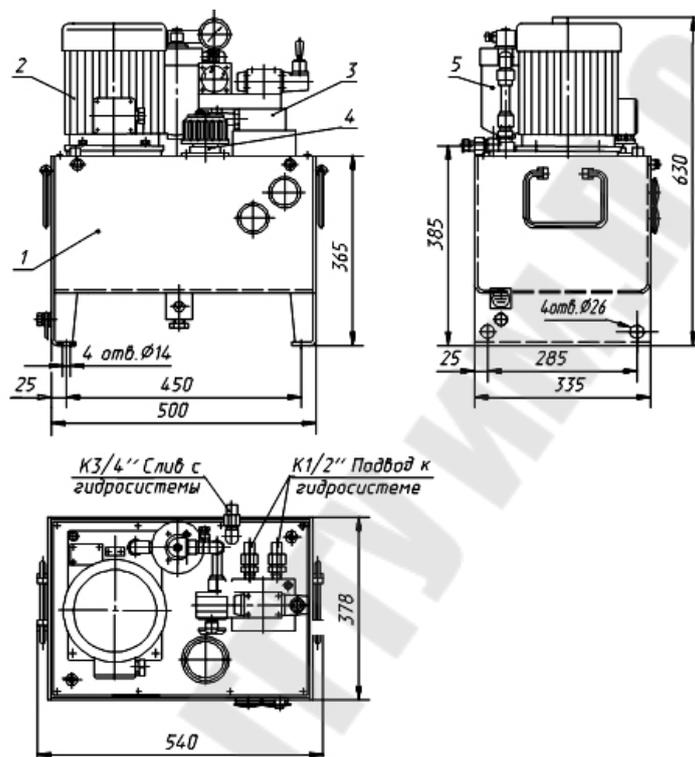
Чертеж станции гидропривода: 1 – гидробак; 2 – насосный агрегат погружного исполнения; 3 – блок управления; 4 – заливной фильтр, совмещенный с сапуном; 5 – напорный фильтр
